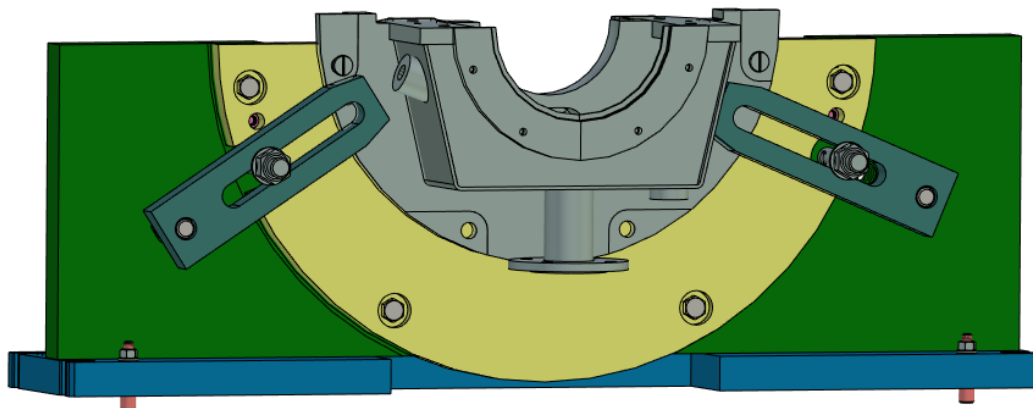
Схема приспособления с деталью «Корпус подшипника».
